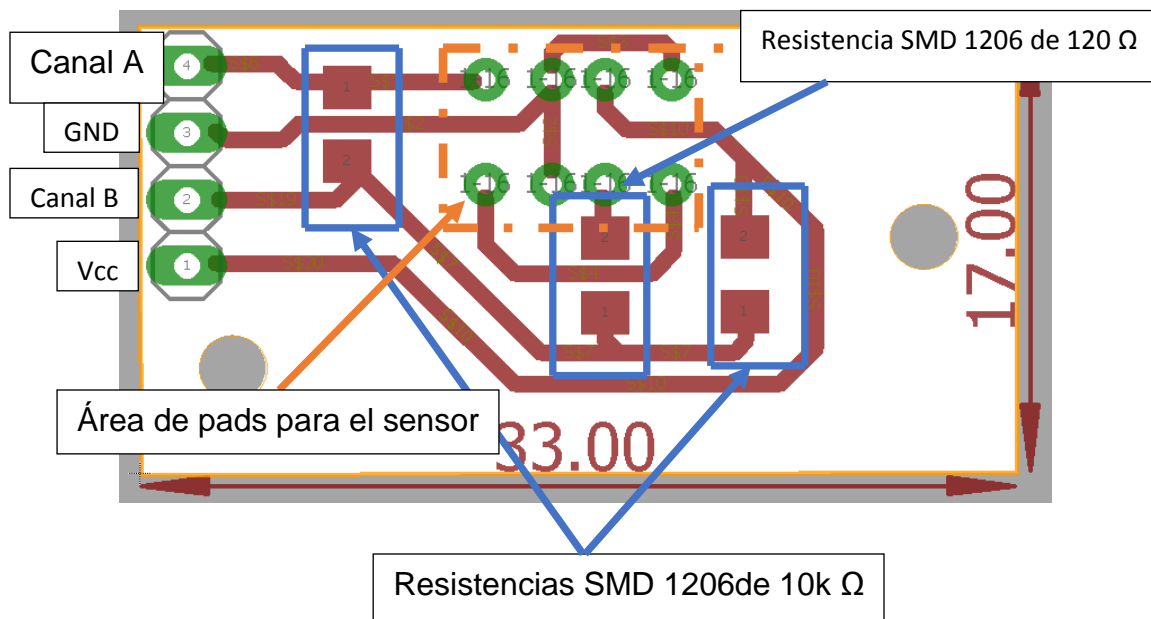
Vista del PCB propuesto para el encoder [FP].
